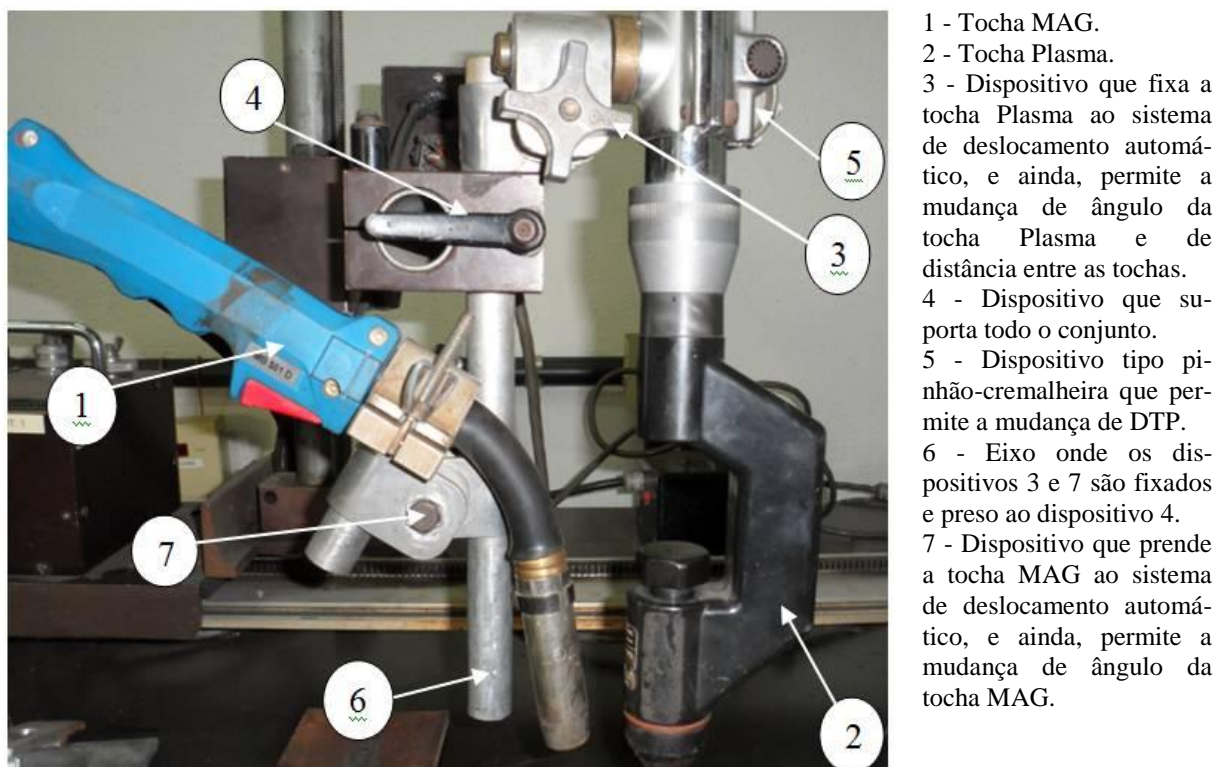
Dispositivo de fixação da tocha Plasma e da tocha MAG no mesmo cabeçote de soldagem
